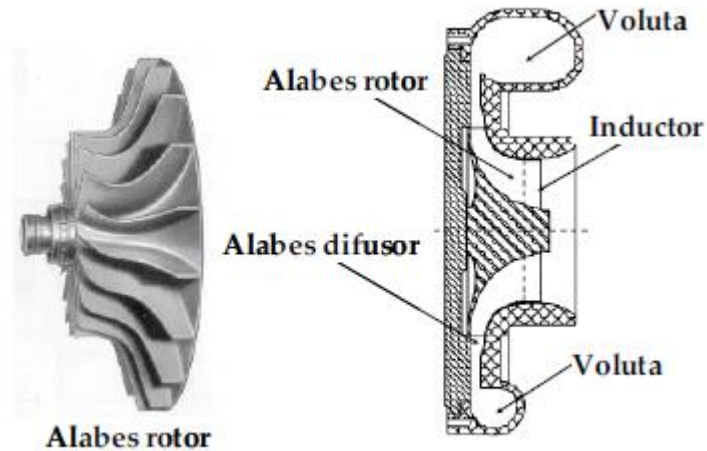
Comportamiento y partes del rotor del turbocompresor.
